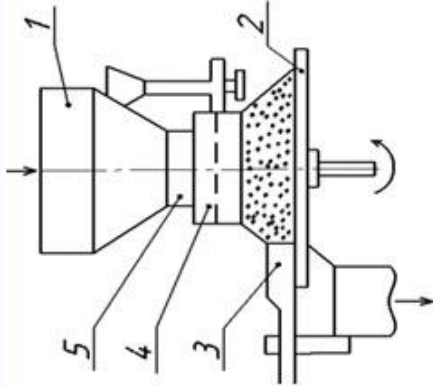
Тарілчастий дозатор: 1 - бункер; 2 - тарілка; 3 - скребок; 4 і 5 - рухомий і нерухомий патрубки
